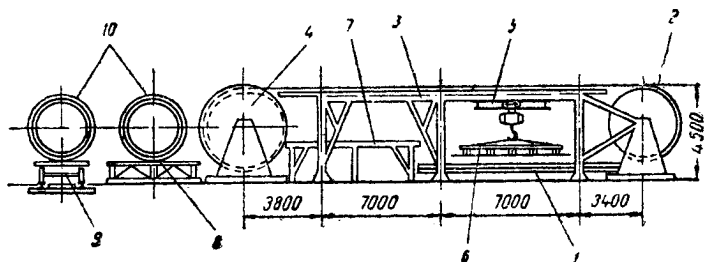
Схема двухъярусной установки для изготовления рулонных конструкций.
